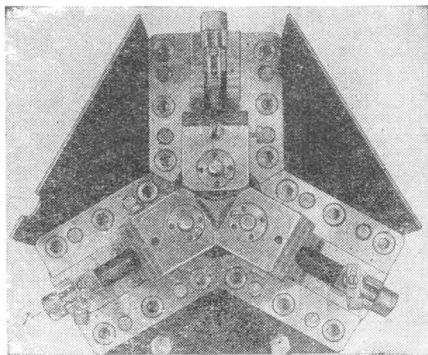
Приспособление для накатывания профиля цилиндрических зубчатых колес на токарном станке.
